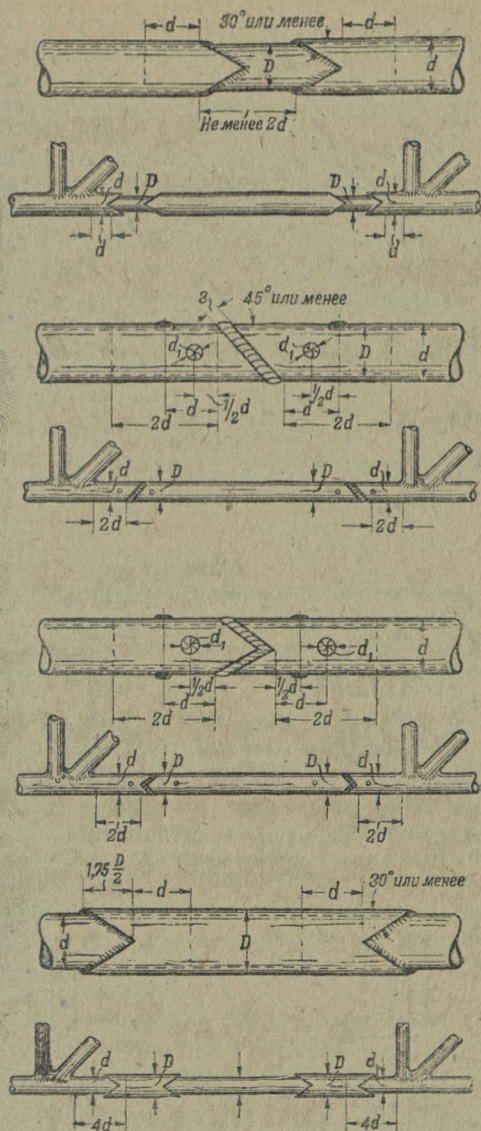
а. Примеры ремонта сварных конструкций самолёта постановкой наружных и внутренних бужей
